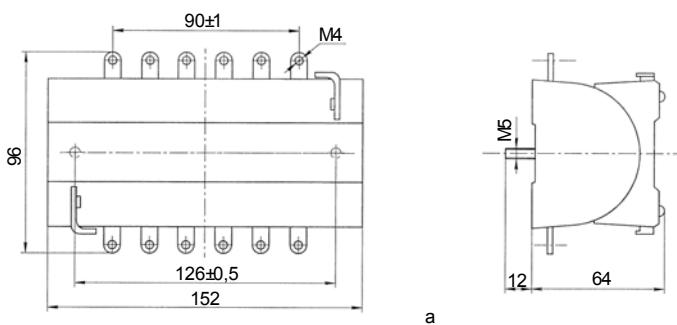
Габаритные размеры штепселя типа ШК 6.
